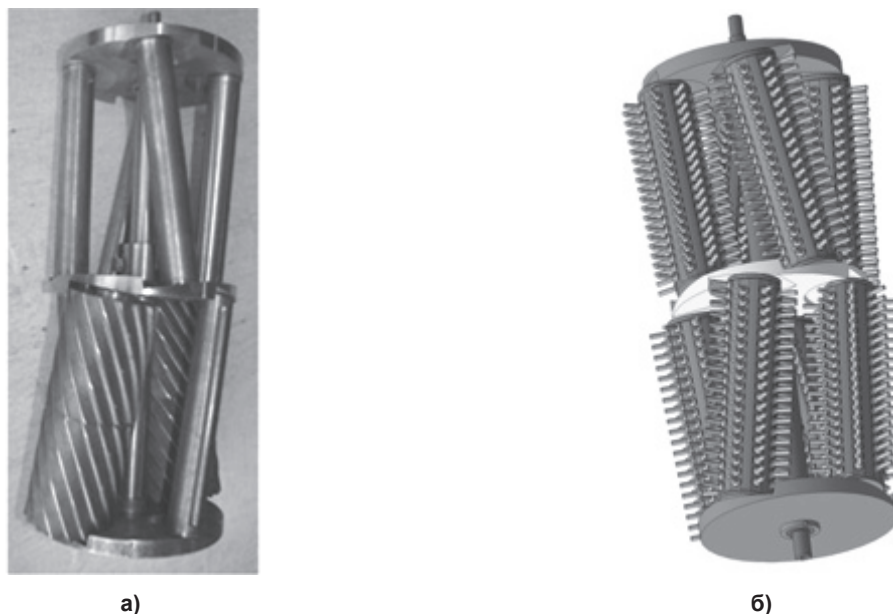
Разработанный фрезерный барабан: а – частично в сборе с червячными фрезами; б – в сборе со столбчатыми режущими элементами
